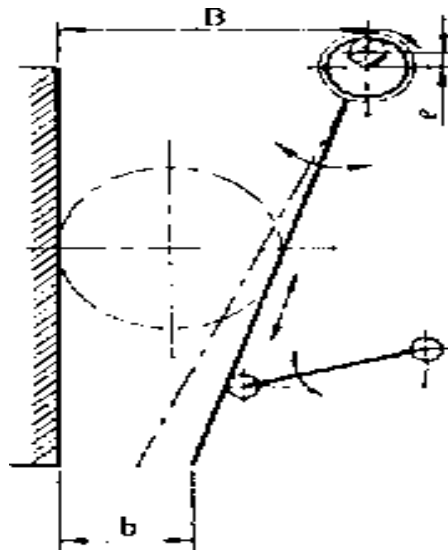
Схема дробарки зі складним коливанням рухомої щокви.
